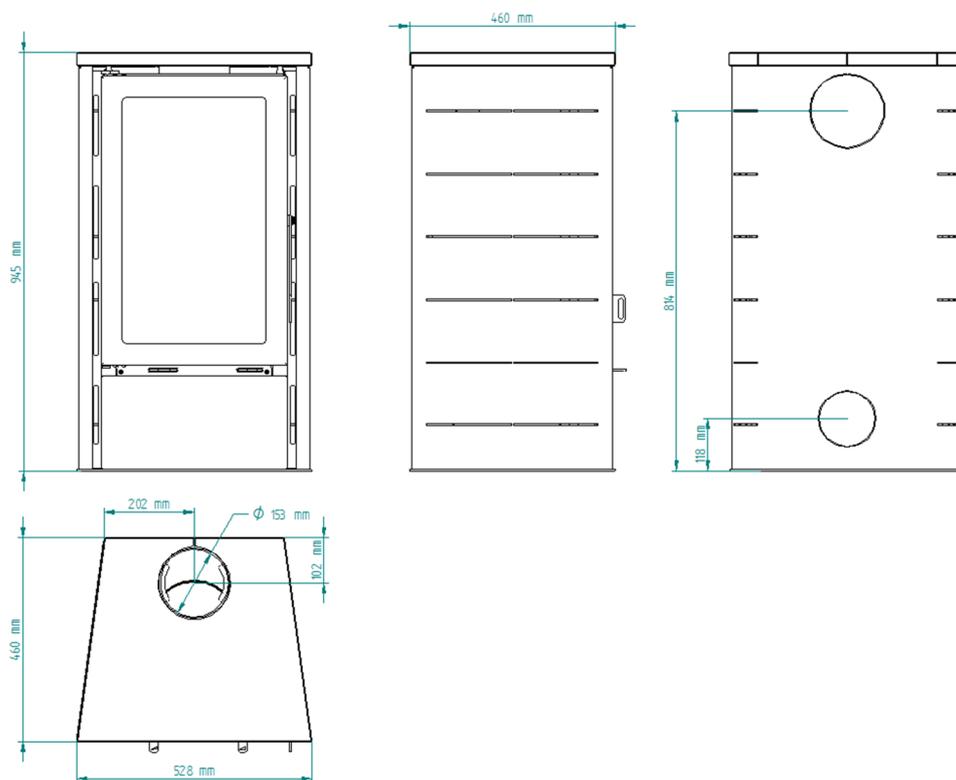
Dimensions générales du poêle à bois Tek Stone
